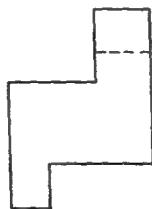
Dibujar el perfil del objeto del que se dan alzado y planta.
